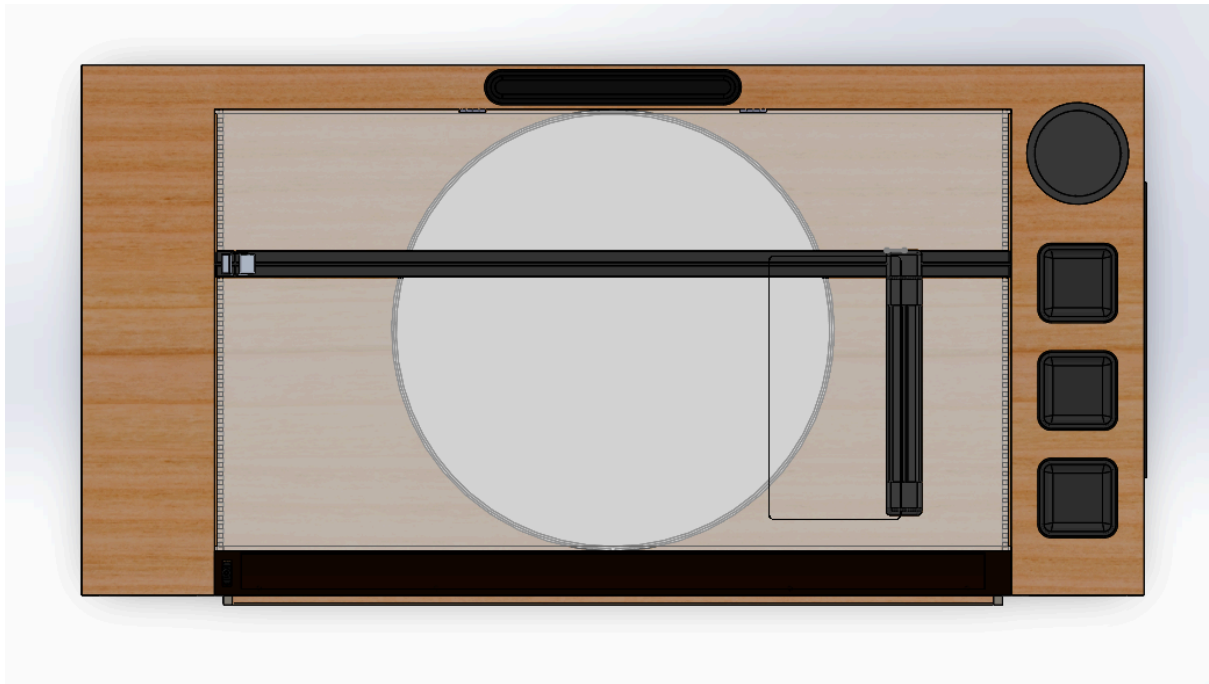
Vista de la Planta del Tablero (Fuente: Elaboración Propia)
